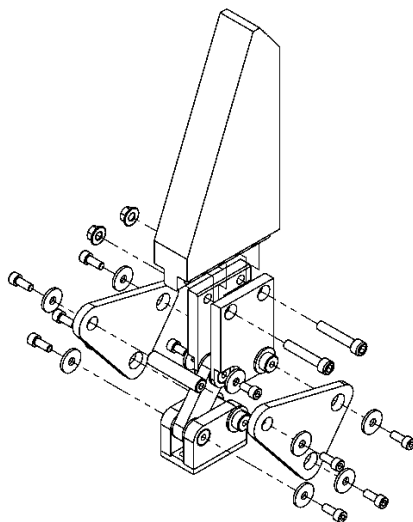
Perspetiva isométrica explodia do desenho de conjunto “Assembly dedo BF”.
